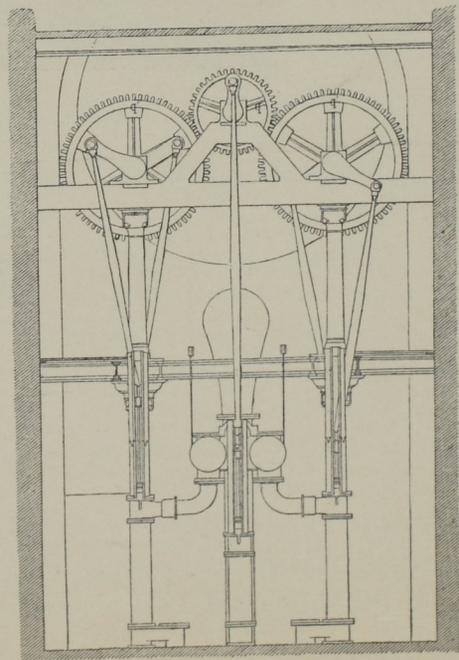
Seitenansicht der Pumpen. Masst. 1 : 90.
